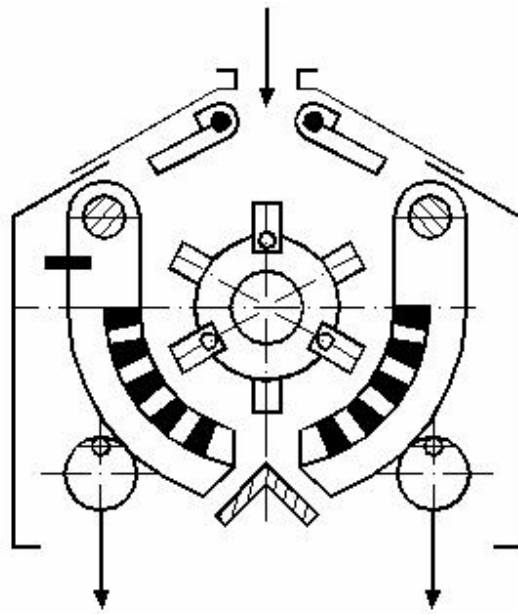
Схема реверсивной дробилки с колосниковыми решетками
